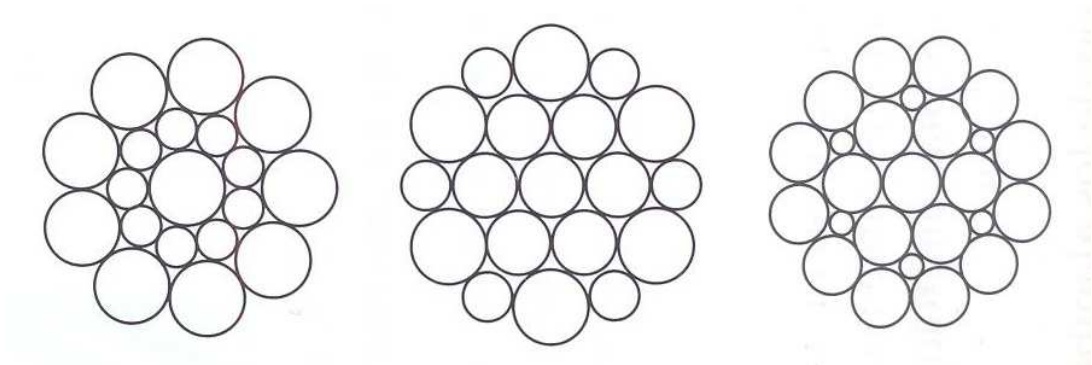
Cables Tipo Seale, Warrington y Filler-Wire, respectivamente
